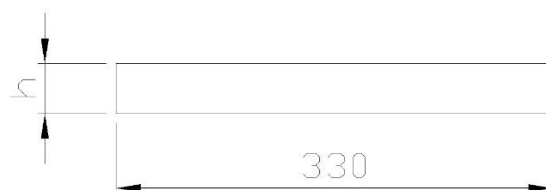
Pormenor das dimensões do bocal de entrada de produto e a regulação da altura "h"
